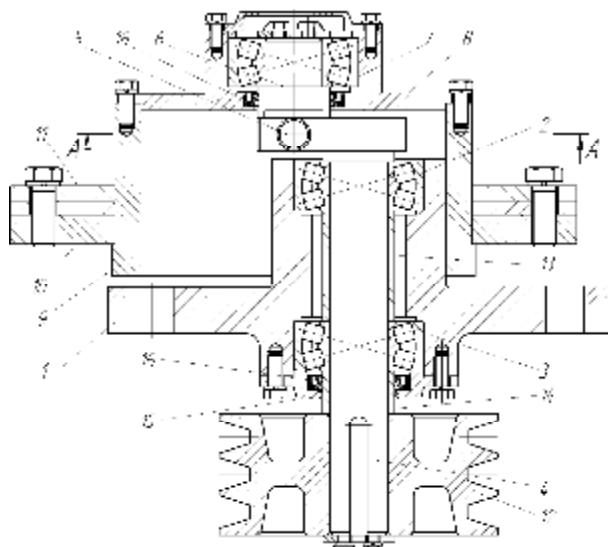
Общий вид планетарного вибровозбудителя круговых колебаний
